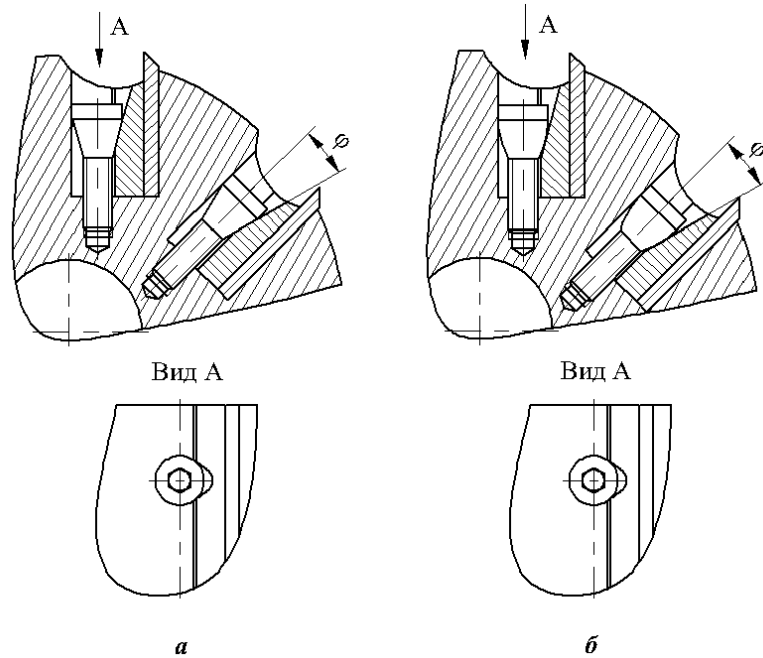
Узел крепления режущего ножа радиальным винтом: *а* – с коническо-цилиндрической головкой; *б* – с криволинейной в осевом сечении головкой
